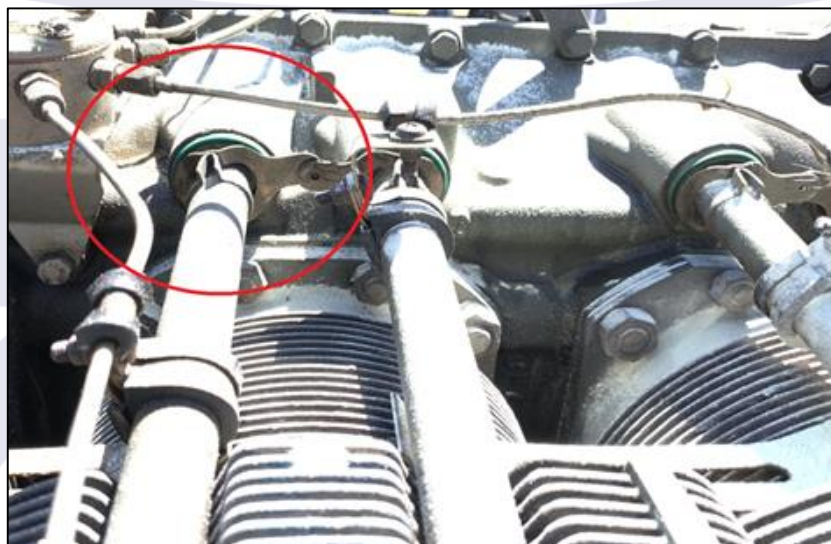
Vista da *Tube Push Rod Shroud* com a respectiva *Spring Shroud Tube* após serem recolocadas e travadas.
